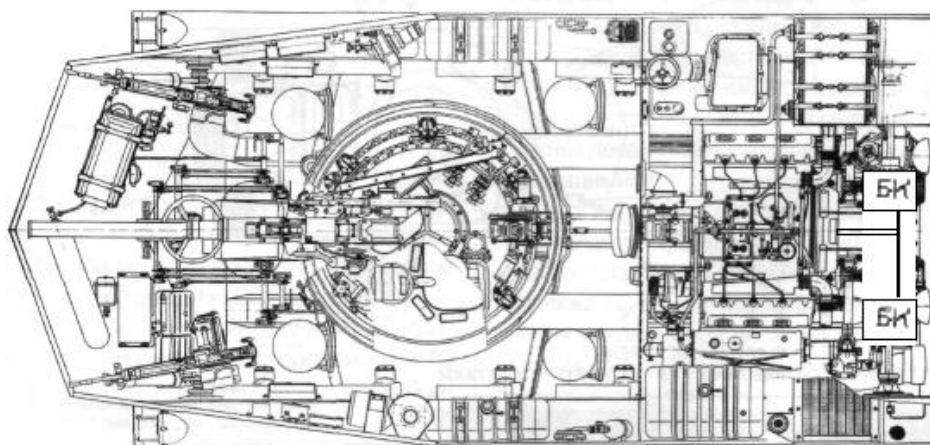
Расположение бортовых коробок в корпусе БМД-Р
